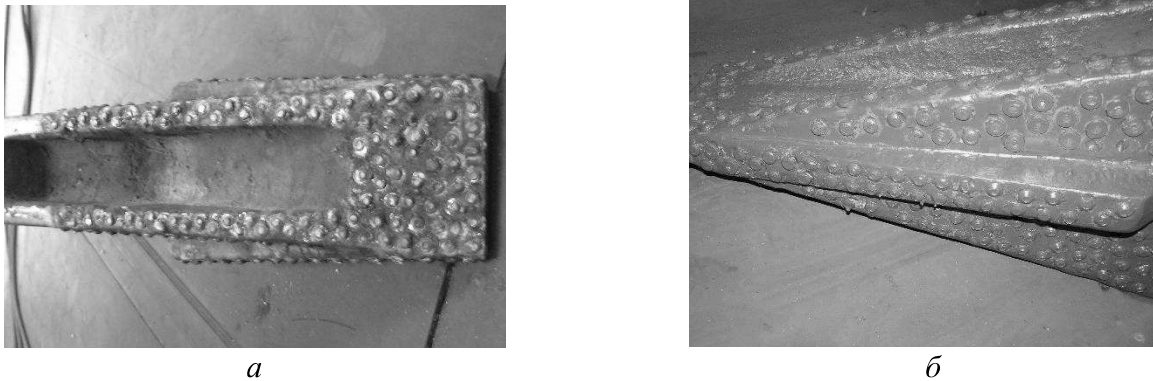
Зуби для ковша екскаватора з нанесеними твердосплавними армуючими елементами: а – поверхні з наплавленими штирями; б – антикорозійне покриття армованих поверхонь
